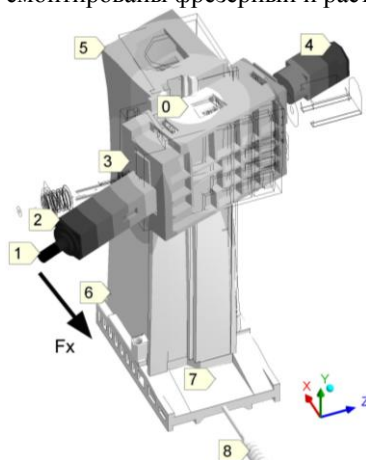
Резонансные крутильные колебания станка (общестаночная мода М3) на частоте 27,8 Гц: 1 – расточной шпиндель; 2 – фрезерный шпиндель внутри горизонтального ползуна (ось Z); 3 – вертикальный суппорт (ось Y); 4 – главный двигатель; 5, 6 – стойка; 7 – салазки (ось X); 8 – образ продольного привода; О – центр крутильных колебаний вокруг вертикальной оси.
